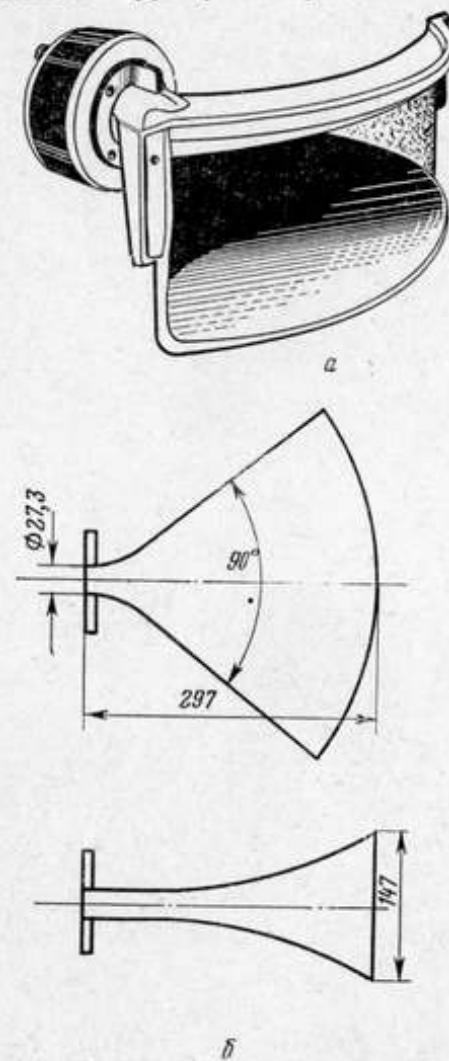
Общий вид (а) и схема (б) рупора с цилиндрическим фронтом волны
